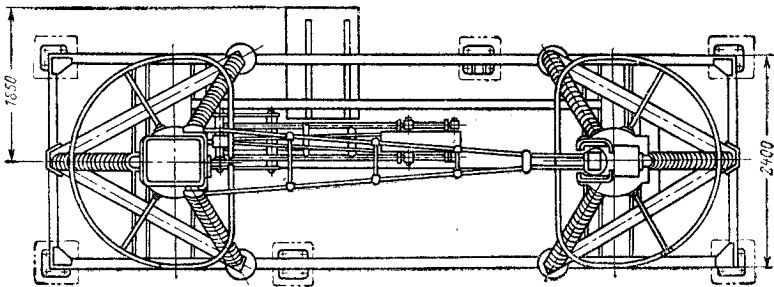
Разъединитель РОН(3)-500/2000.
